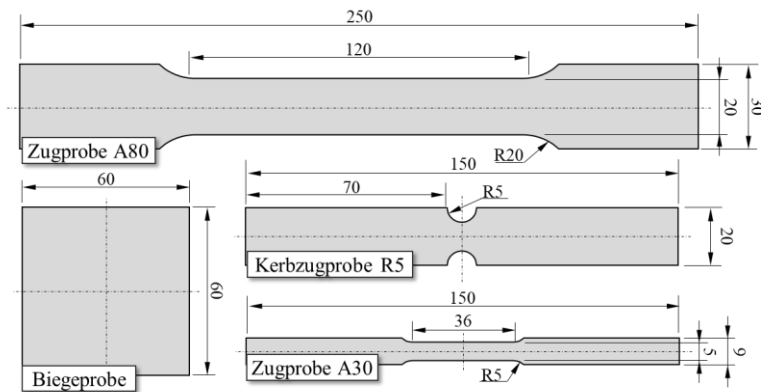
Übersicht der verwendeten Probengeometrien für die Versuche an der Universalprüfmaschine Zwick Z100
